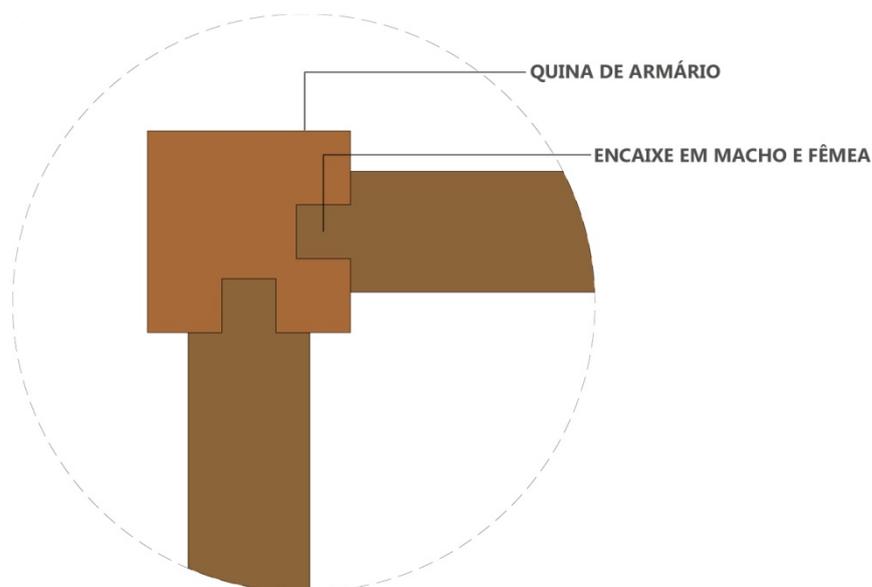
Quina de armário estruturado com junções dos painéis de vedação em macho e fêmea.
